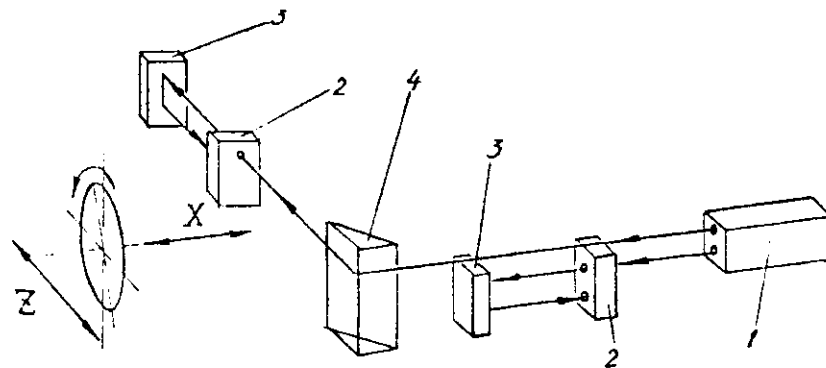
Симметричный чертёж светового токарного станка мод. 43652123.04 и кинематика рабочих движений:
